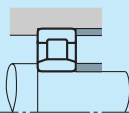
Disposición de montaje y tipos de rodamientos
